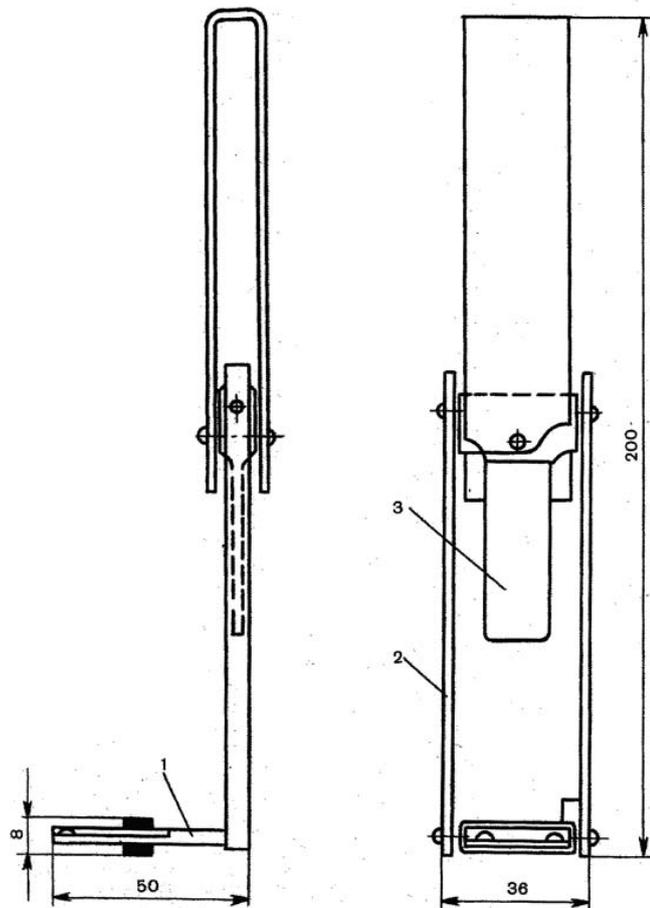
Приспособление для проверки катушечного высевяющего аппарата сеялки: 1 — линейка; 2 — корпус; 3 — щуп
